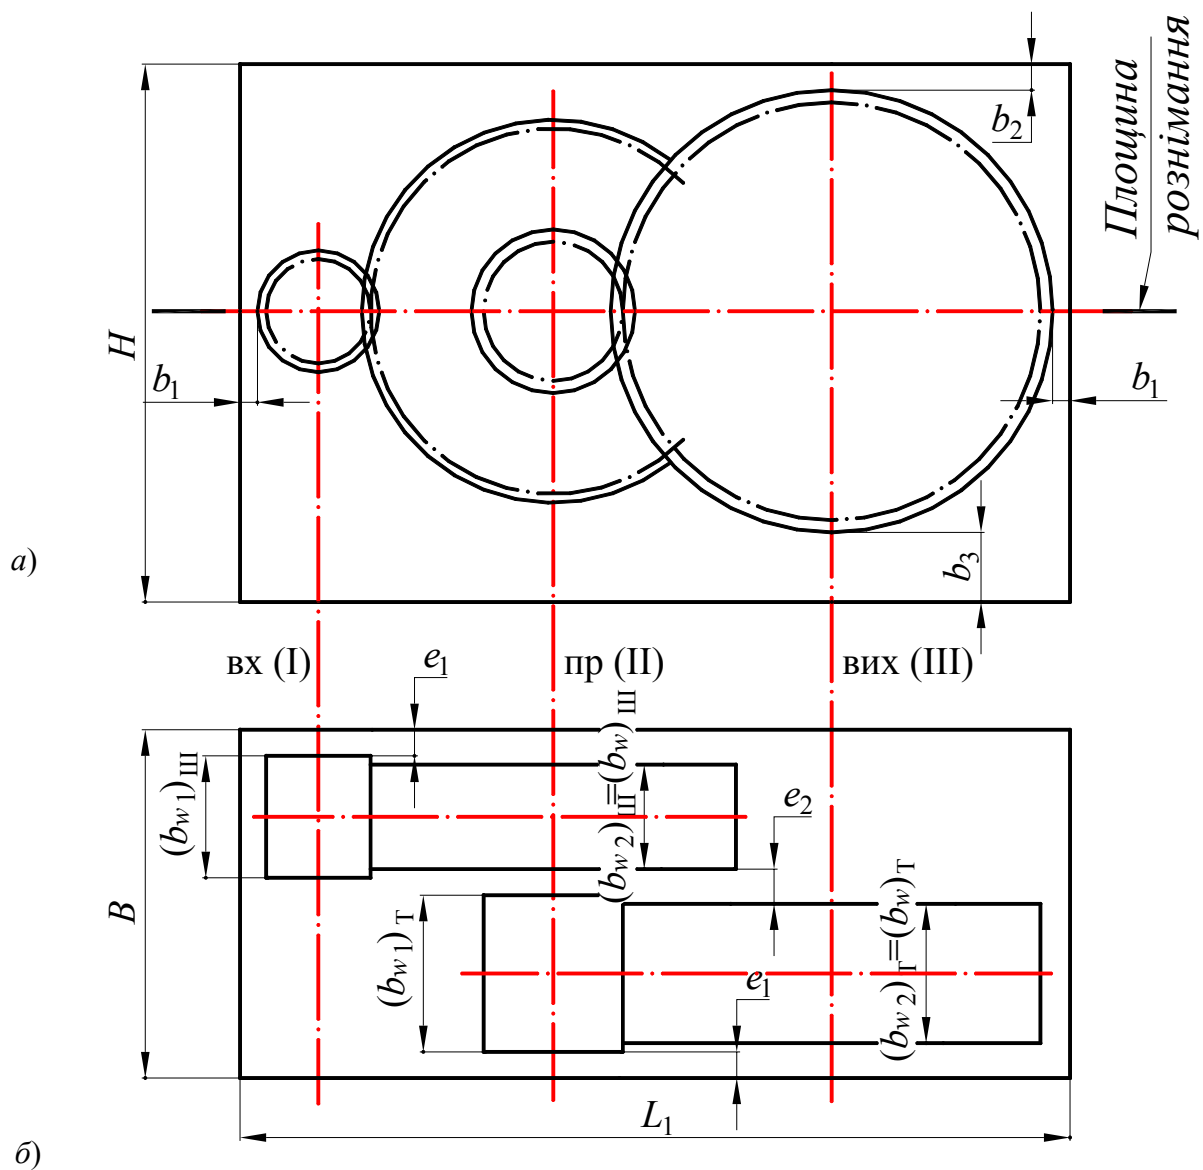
Перший етап ескізного компоунання двоступінчастого циліндричного редуктора за розгорнутою схемою
